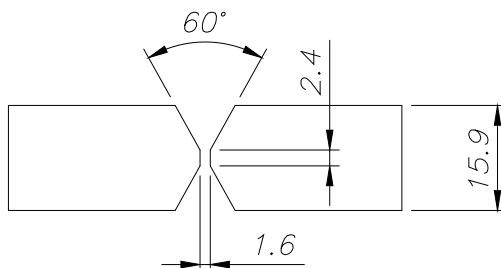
Secção transversal das juntas que foram soldadas – chanfro tipo “duplo V”.
